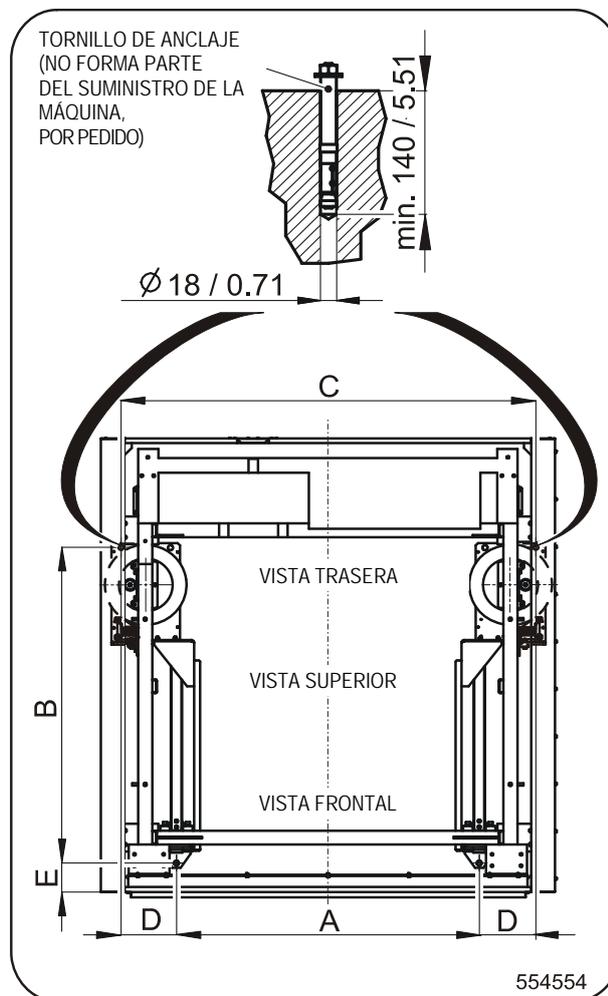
K Máquina 80-100-120 kg / 180-230-275 lbs con la inclinación delantera y sistema de pesado, puesto del taladrado para tornillos de anclaje, (dimensiones en mm / pulgada)
